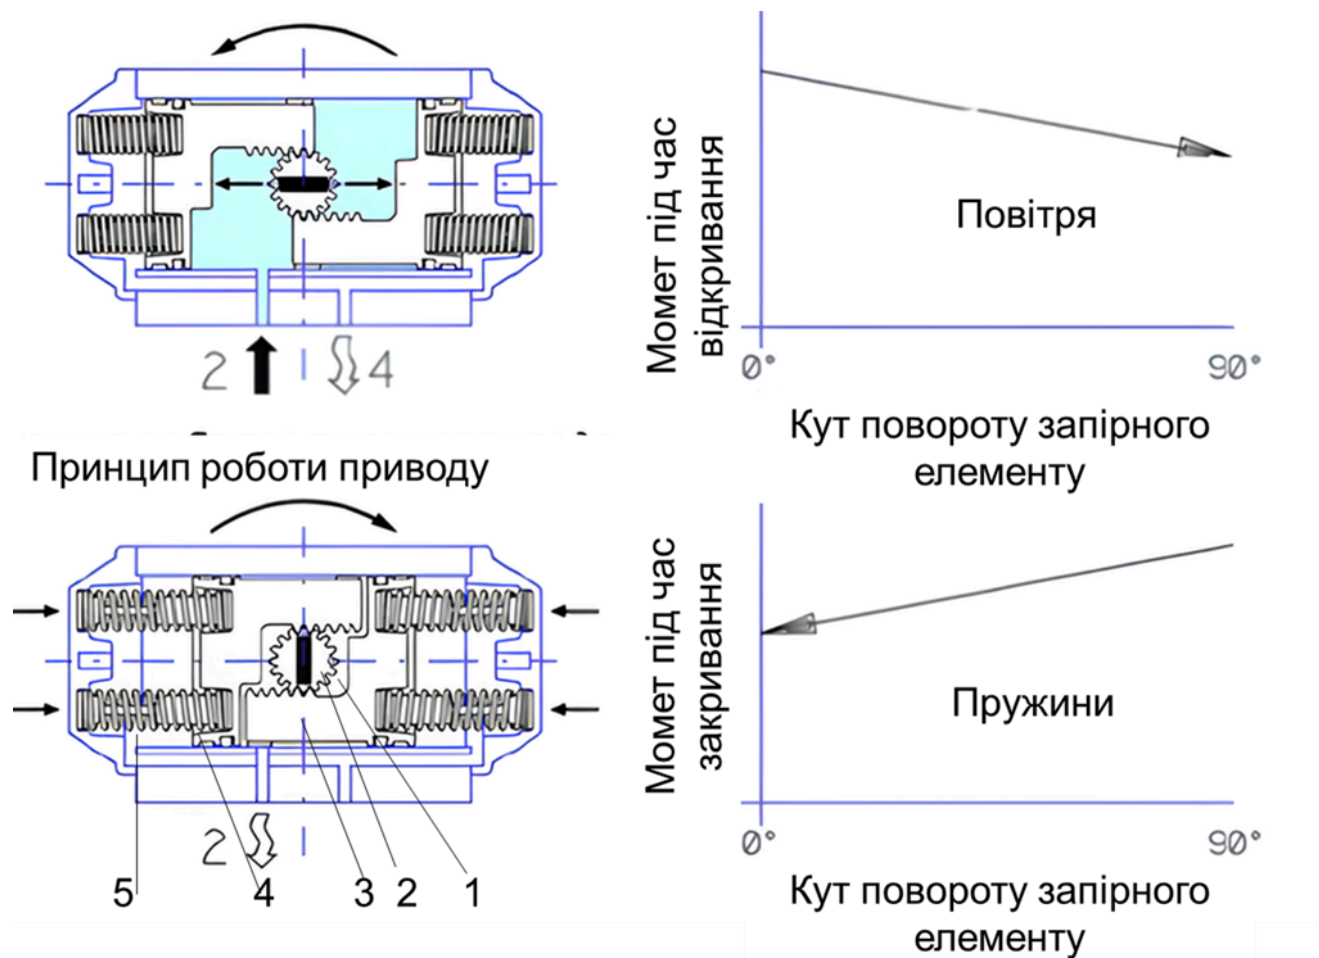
Привід пневматичний поворотний: 1- маточина; 2 – вал з шестернею; 3 – рейка із зубцями; 4- поршень; 5 – пружина повернення в початкове положення.
